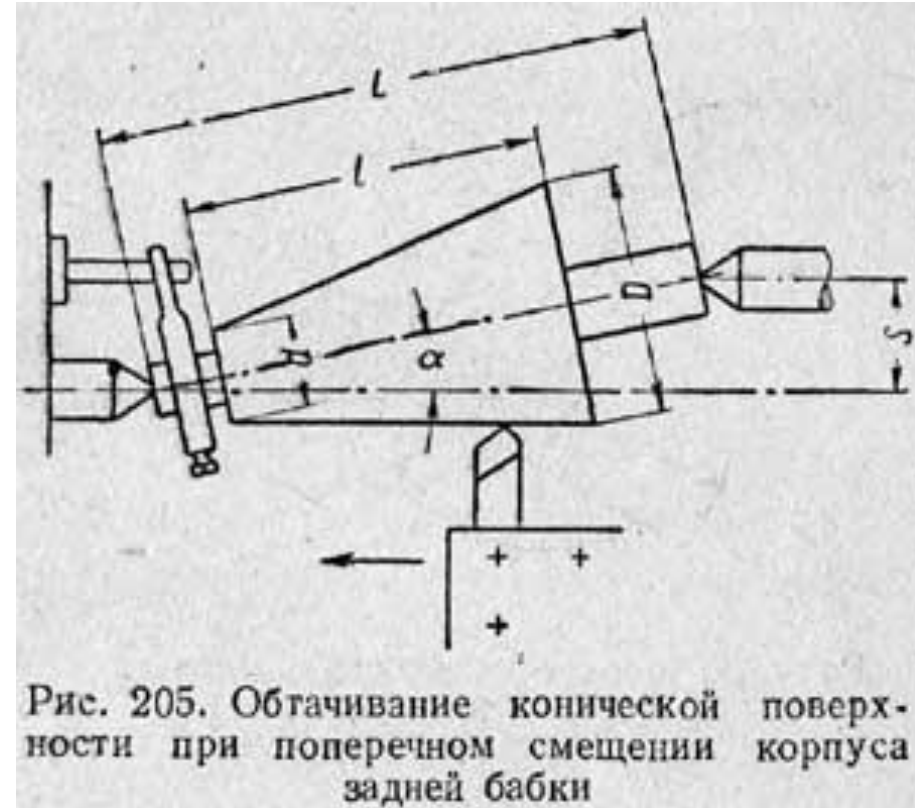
Обтачивание конической поверхности при поперечном смещении корпуса задней бабки
